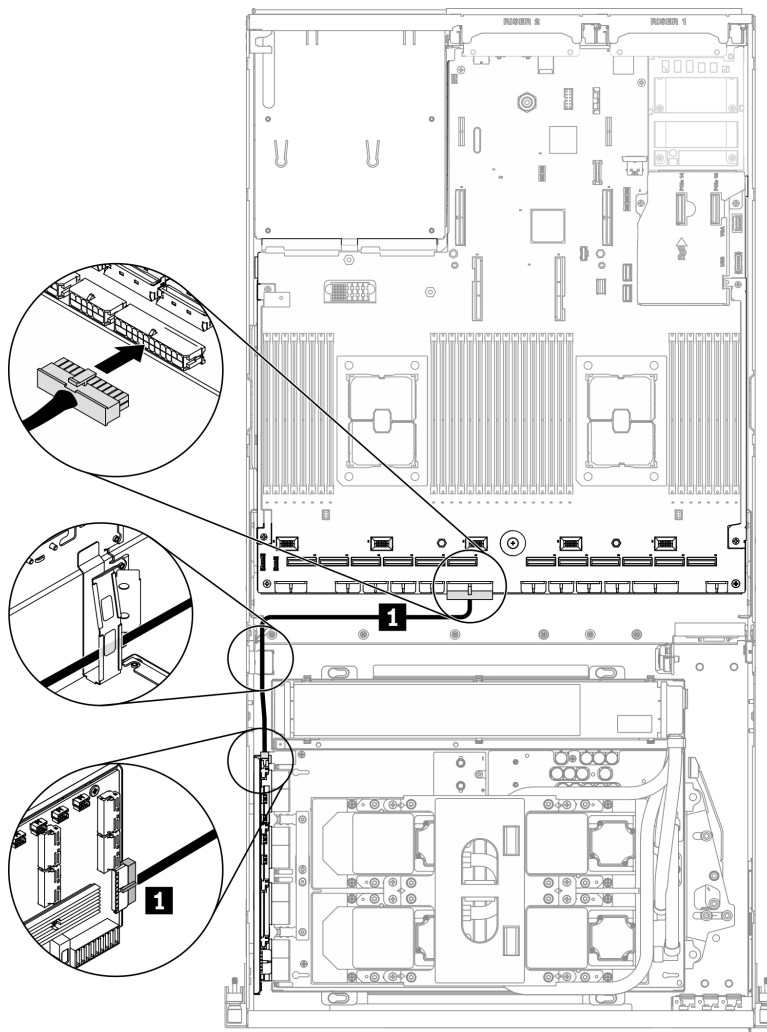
Anschließen des Pumpenkabels der Retimer-Baugruppe
